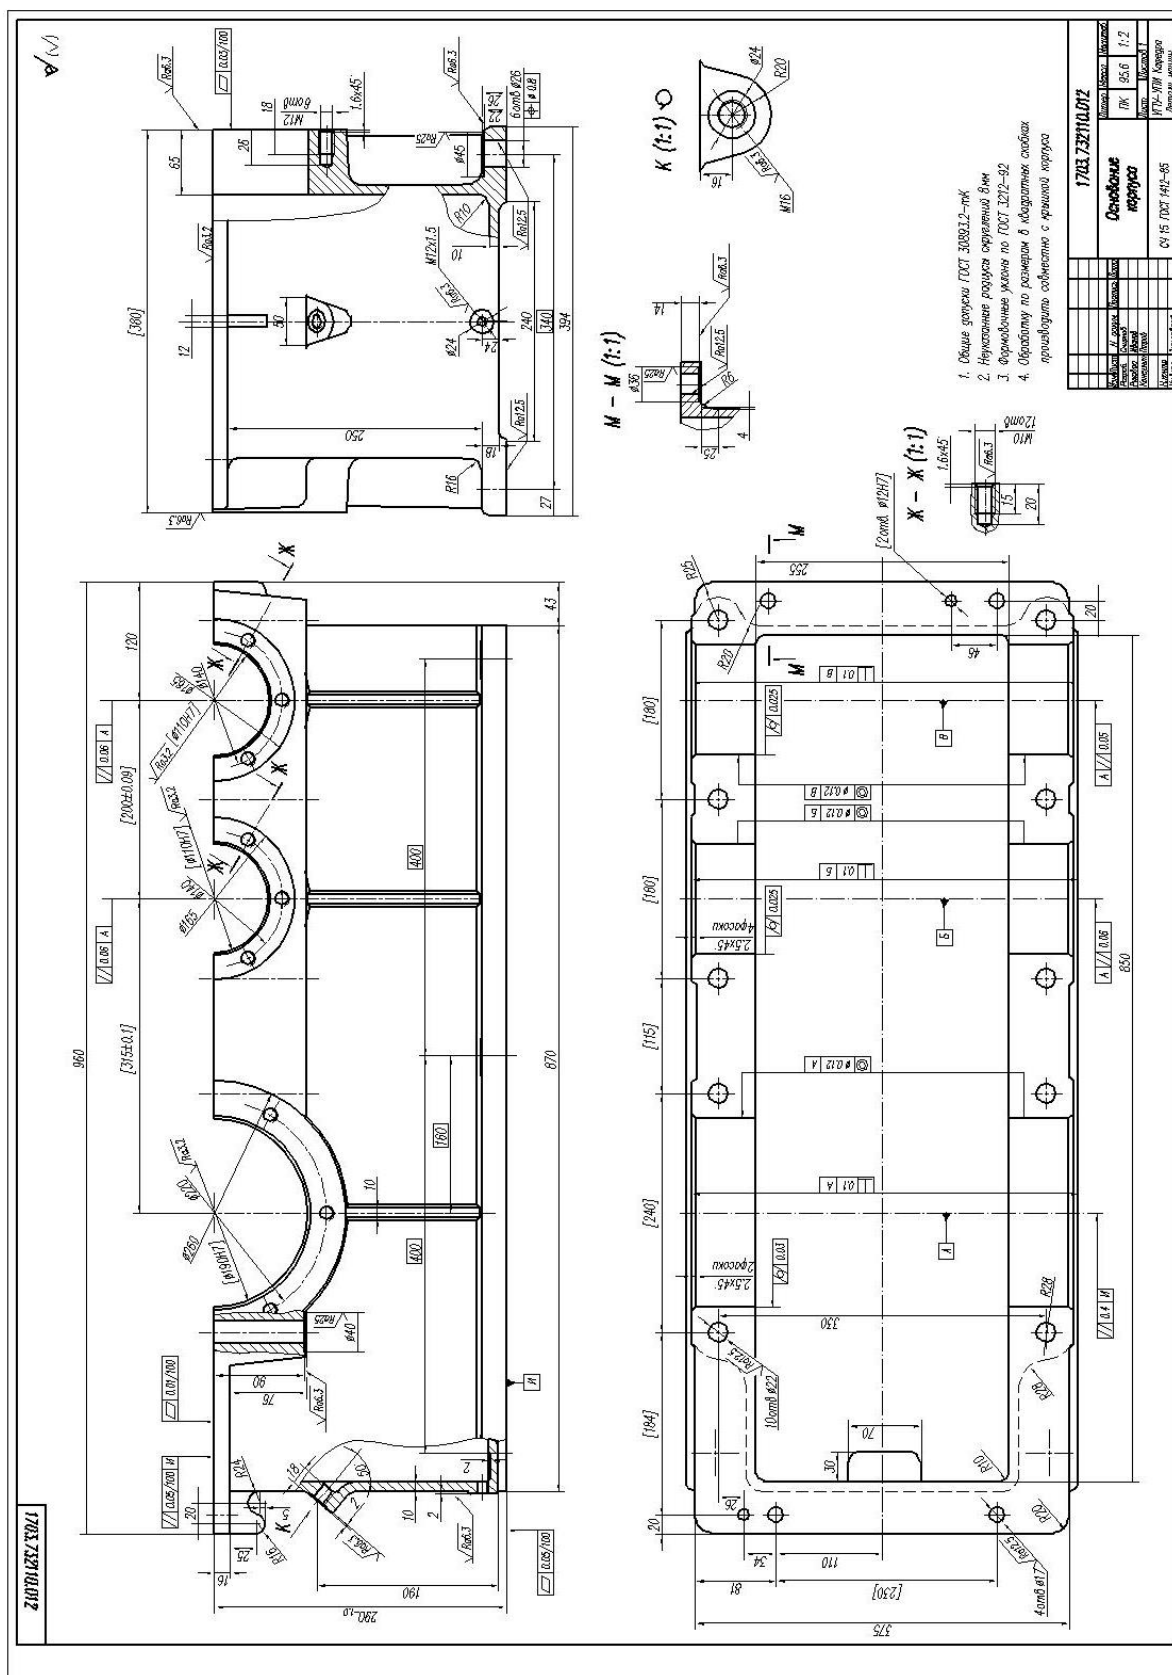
Рабочий чертеж основания корпуса цилиндрического двухступенчатого редуктора
